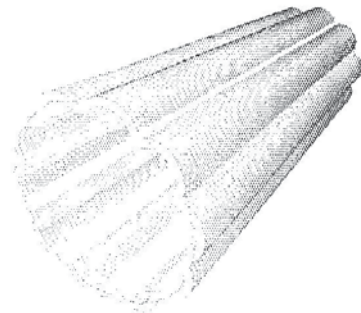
Фильтрующая труба, получаемая из продольно-гофрированной металлической заготовки
